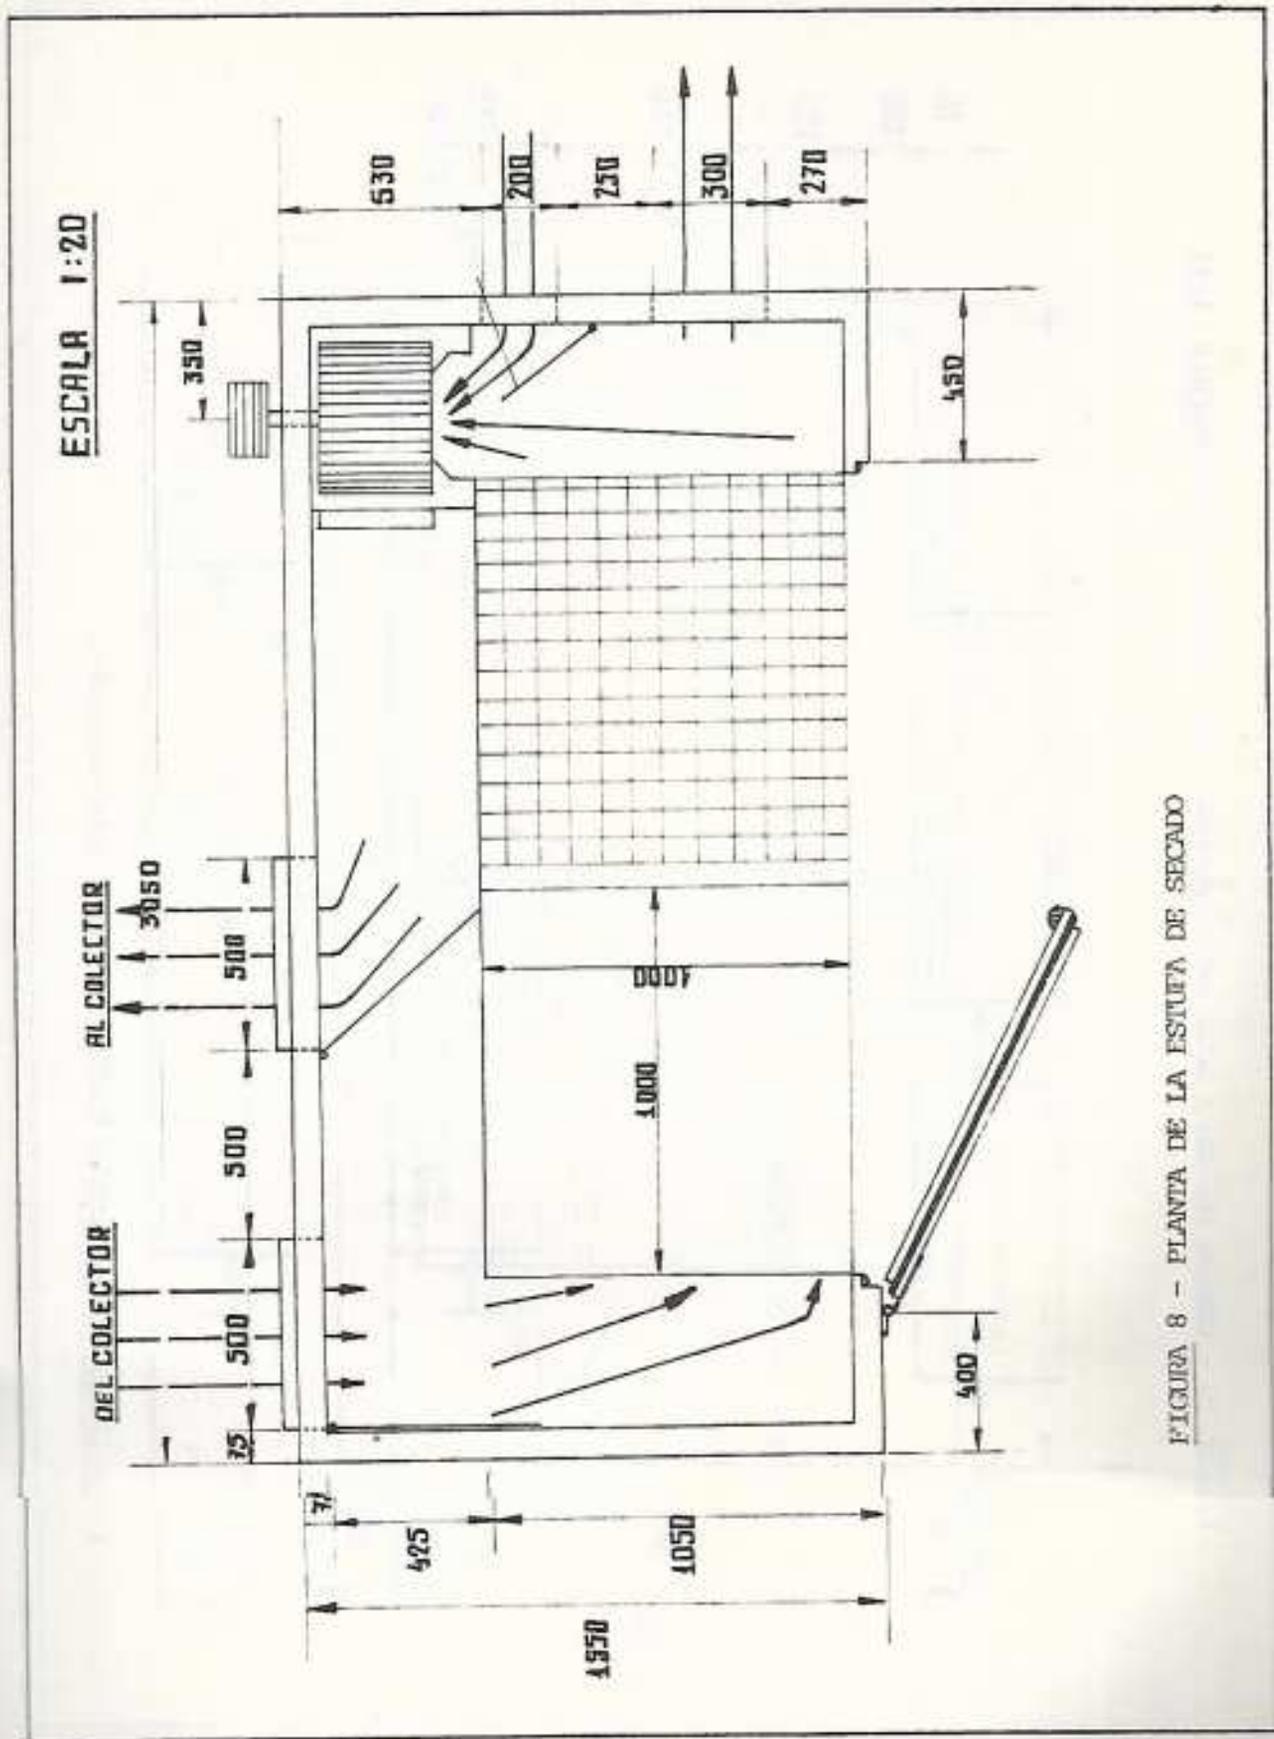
PLANTA DE LA ESTUFA DE SECADO
